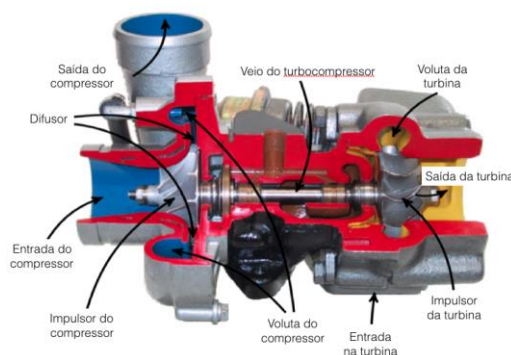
Componentes que constituem um turbocompressor, Leufvén (2013).
